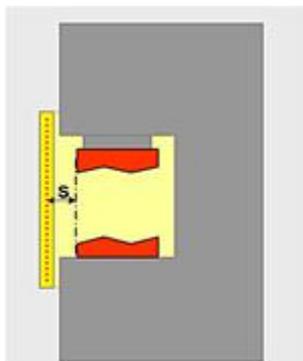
Distanza di sicurezza della barriera rispetto al punto
